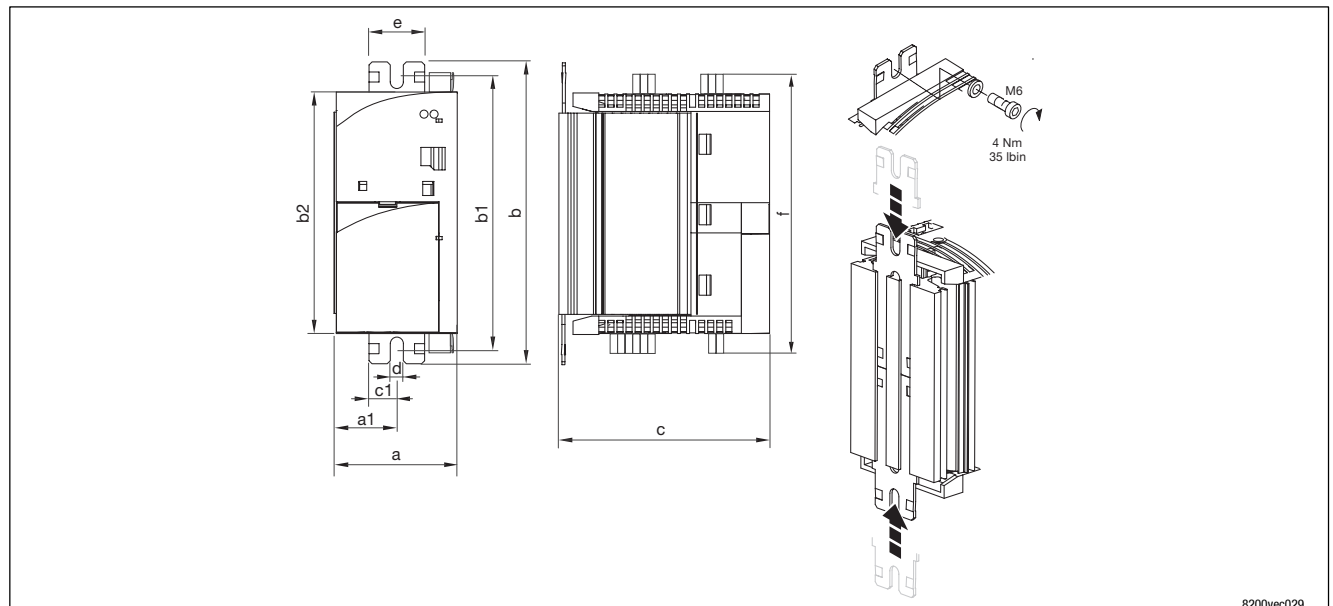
Encombrements : Montage en technique "Cold Plate" - plaque de refroidissement 0,25 ... 2,2 kW
